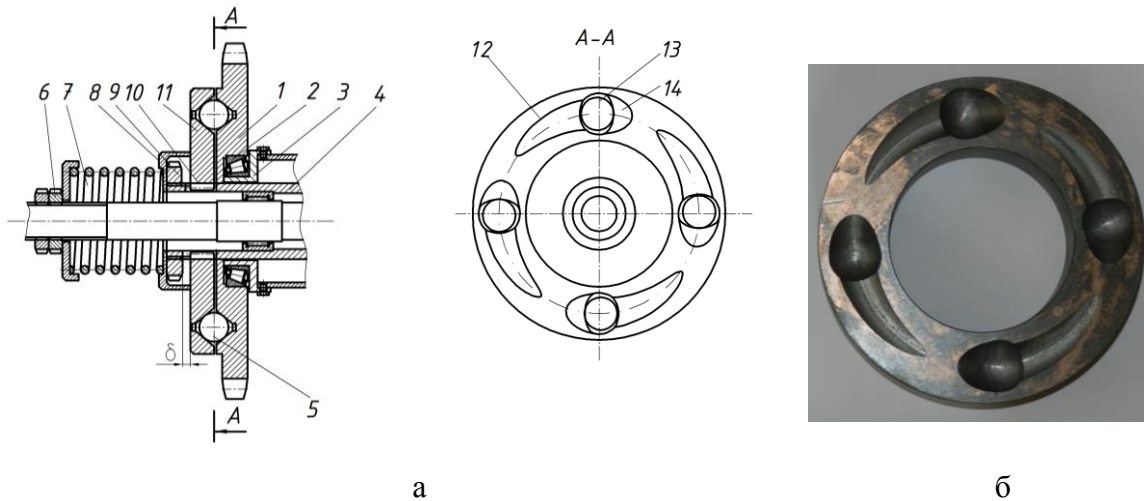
Конструктивна схема запобіжної муфти (а) та загальний вигляд робочої поверхні веденої півмуфти (б): 1 – ведуча півмуфта; 2 – радіально – упорний підшипник; 3 – корпус; 4 – вал шнека; 5 – кульки; 6 – гайка; 7 – цент-ральна пружина; 8 – втулка; 9 – гайка; 10 – шліци; 11 – ведена півмуфта; 12 – похила робоча канавка; 13 – лунки; 14 - похила зворотна канавка
